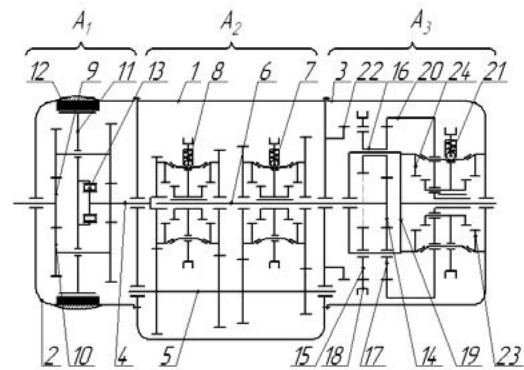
Кинематическая схема многоступенчатой коробки передач: A1 — дифференциальный делитель; A2 — основной редуктор; A3 — дифференциальный демультипликатор; 1 — корпус основного редуктора; 2 — картер сцепления (картер дифференциального делителя); 3 — картер дифференциального демультипликатора; 4 — первичный вал основного редуктора; 5 — промежуточный вал основного редуктора; 6 — вторичный вал основного редуктора; 7 и 8 — синхронизаторы первой-второй и третьей-четвёртой передач основного редуктора соответственно; 9 — входной вал-шестерня дифференциального делителя; 10 — двухвенцовые сателлиты дифференциального делителя; 11 — водило дифференциального делителя; 12 — ленточные тормоза; 13 — муфта свободного хода; 14 — ведущий зубчатый венец дифференциального демультипликатора; 15 — сателлиты дифференциального демультипликатора; 16 — двухвенцовые сателлиты дифференциального демультипликатора; 17 — паразитные сателлиты дифференциального демультипликатора; 18 — коронное колесо (муфта заднего хода) дифференциального демультипликатора; 19 — водило дифференциального демультипликатора (выходной вал коробки передач); 20 — коронное колесо дифференциального демультипликатора; 21 — синхронизатор дифференциального демультипликатора; 22 — зубчатый венец блокировки муфты заднего хода; 23 — зубчатый венец блокировки коронного колеса дифференциального демультипликатора; 24 — зубчатый венец блокировки дифференциального демультипликатора
